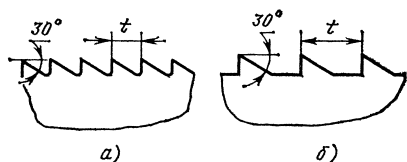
Форма зубьев ленточных пил для сталей (а) и цветных металлов (б)
